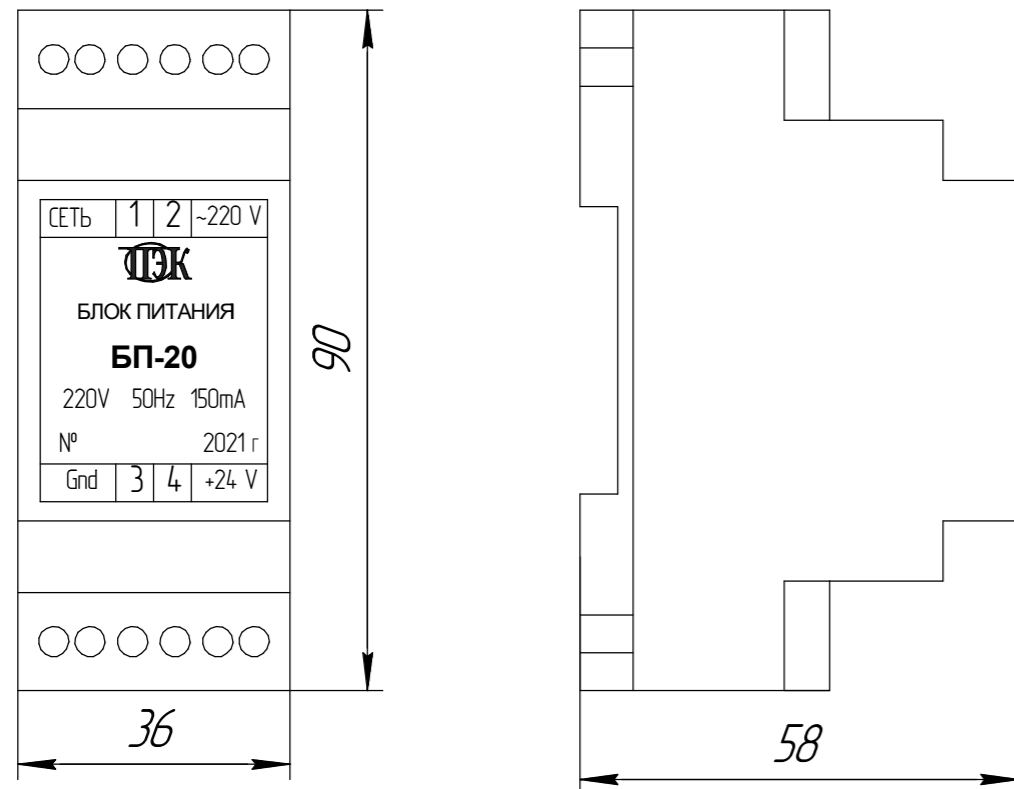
Габаритные размеры блока БП-20 на DIN-рейке
